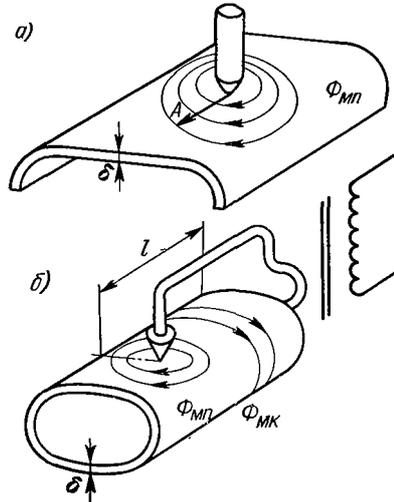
Магнитные потоки в свариваемых деталях:
